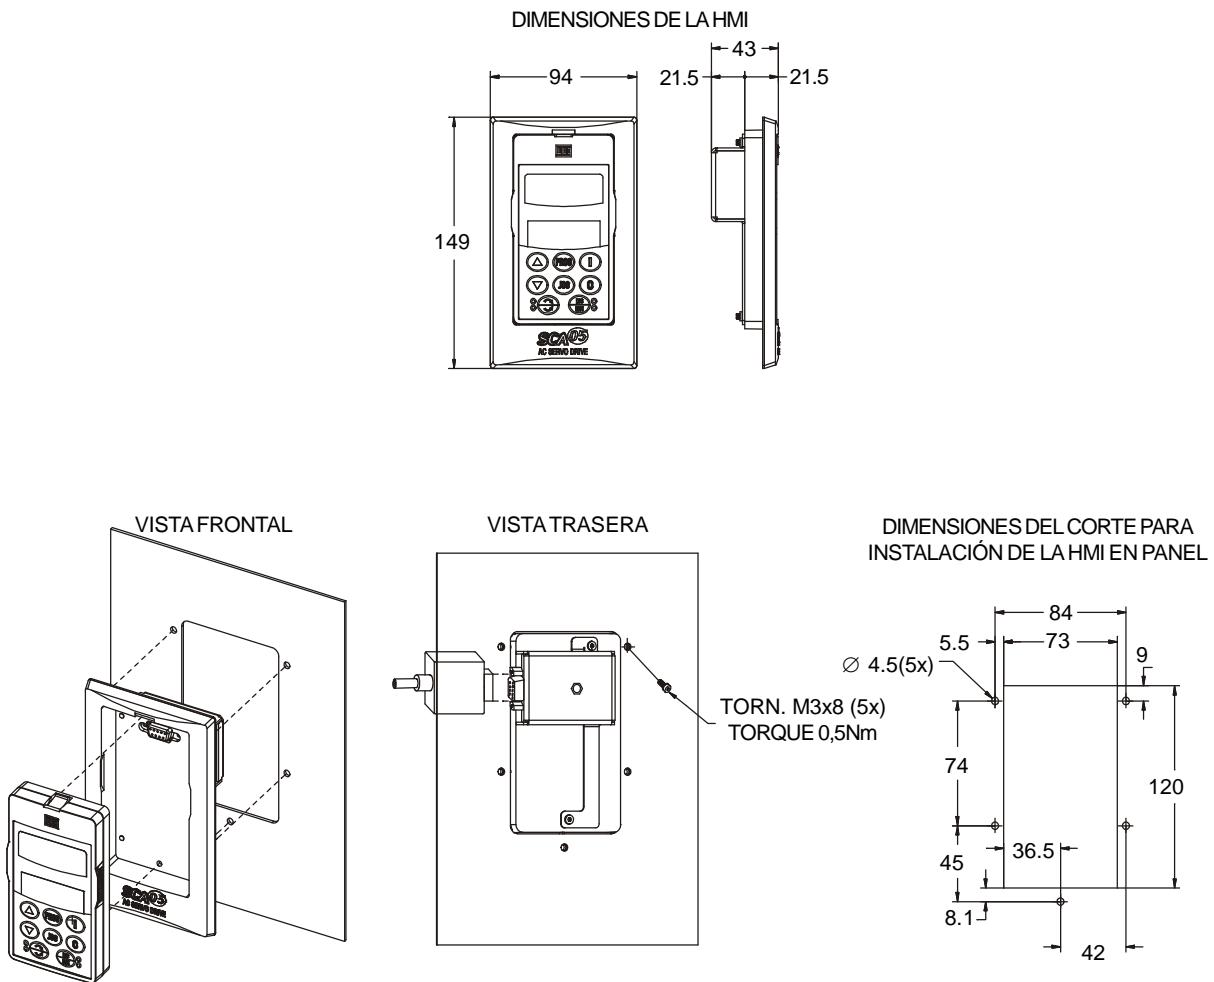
HMI - Dimensiones y instalación en tablero (mm)
